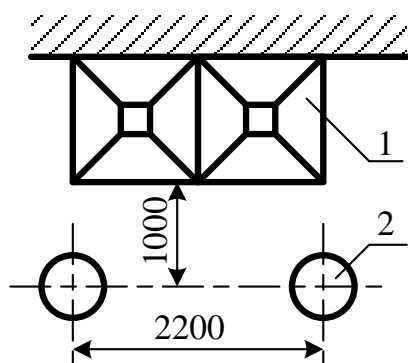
Схемы расположения наковален и горнов при ручной ковке:
